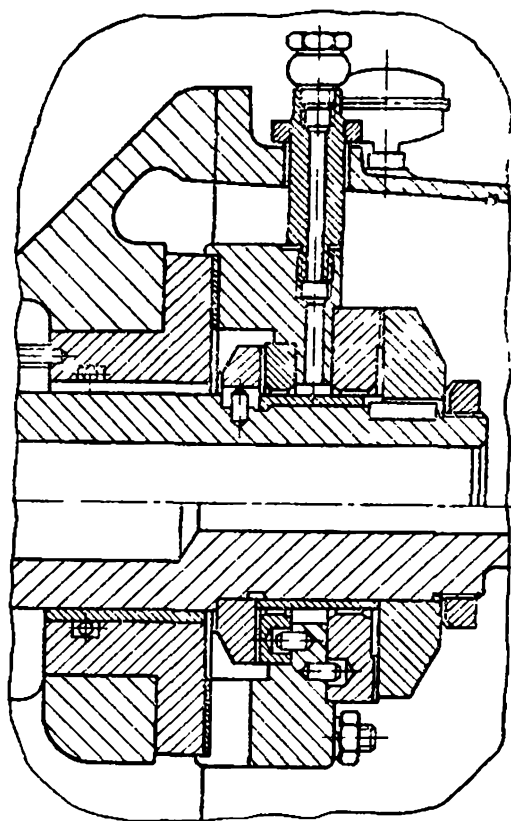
Двусторонний сегментный осевой подшипник завода ЧКД (Прага)
